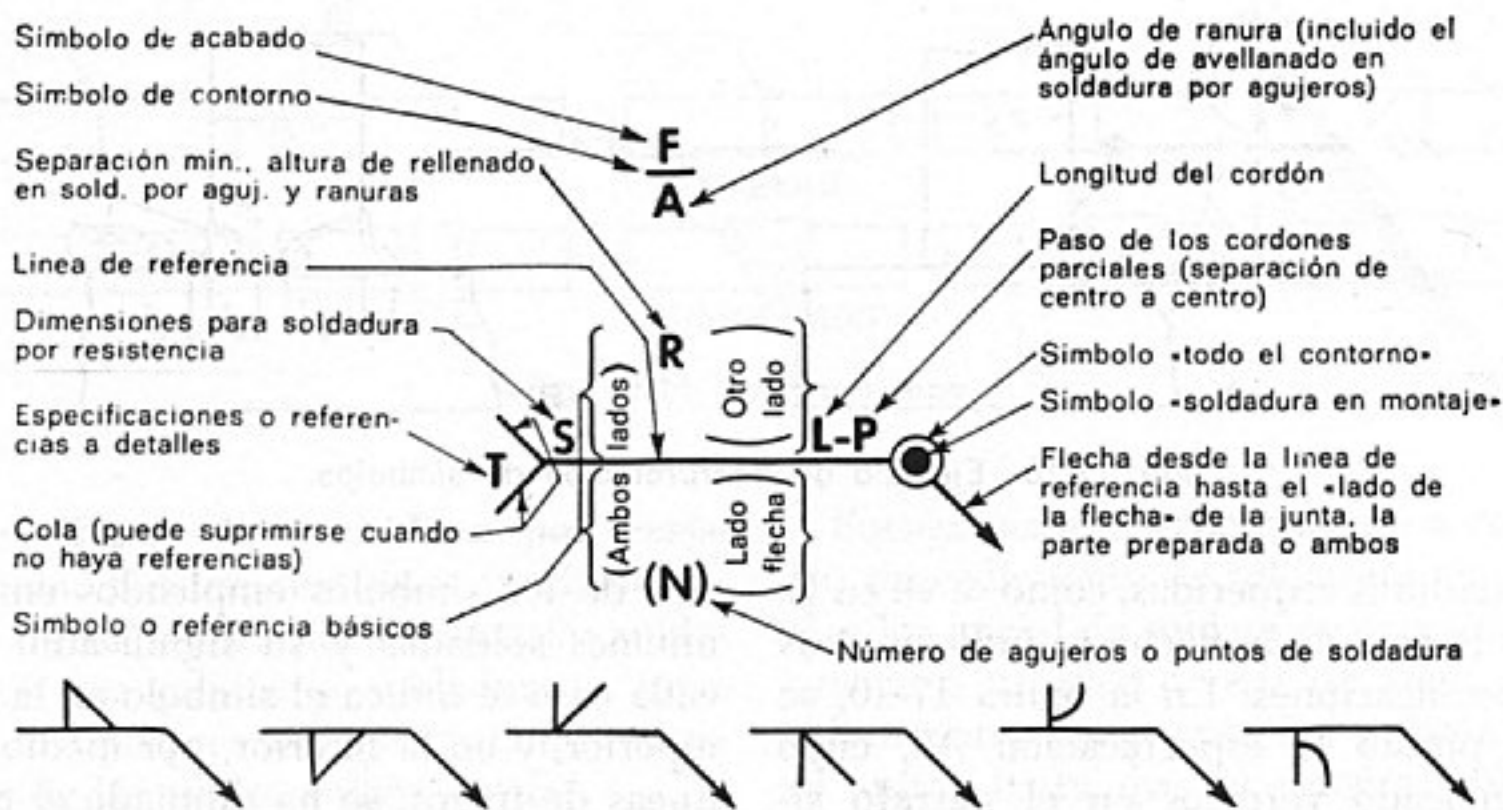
Colocación de la información en los símbolos de soldadura.
